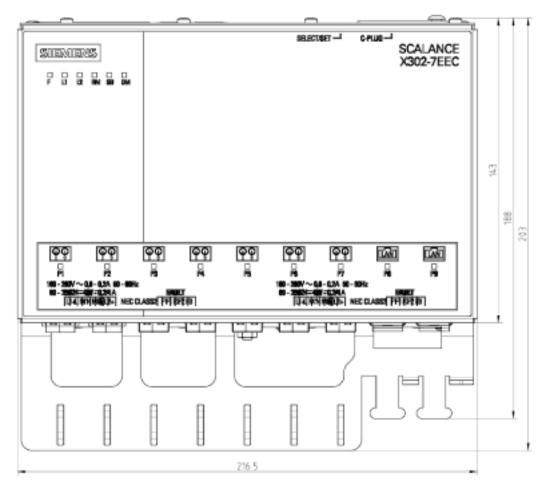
Dessin coté du switch IE X302-7EEC - Vu de face
